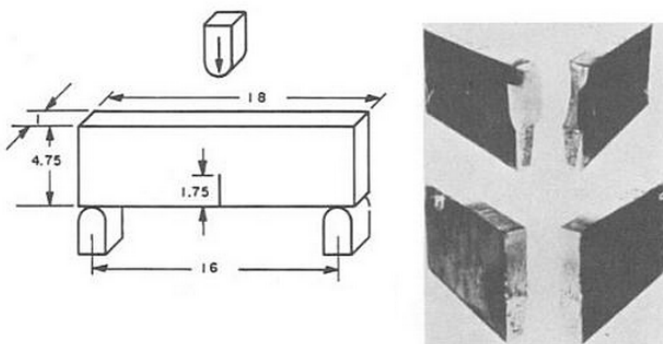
Příklad zkoušky rázem v ohybu velkých těles původní tloušťky [34].
